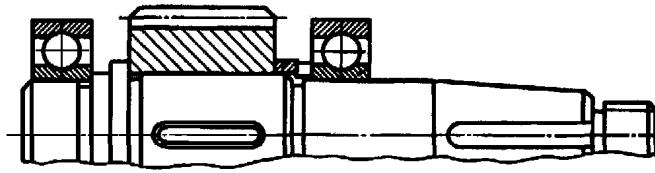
Вал цилиндрической передачи в сборе с шестерней и подшипниками качения
